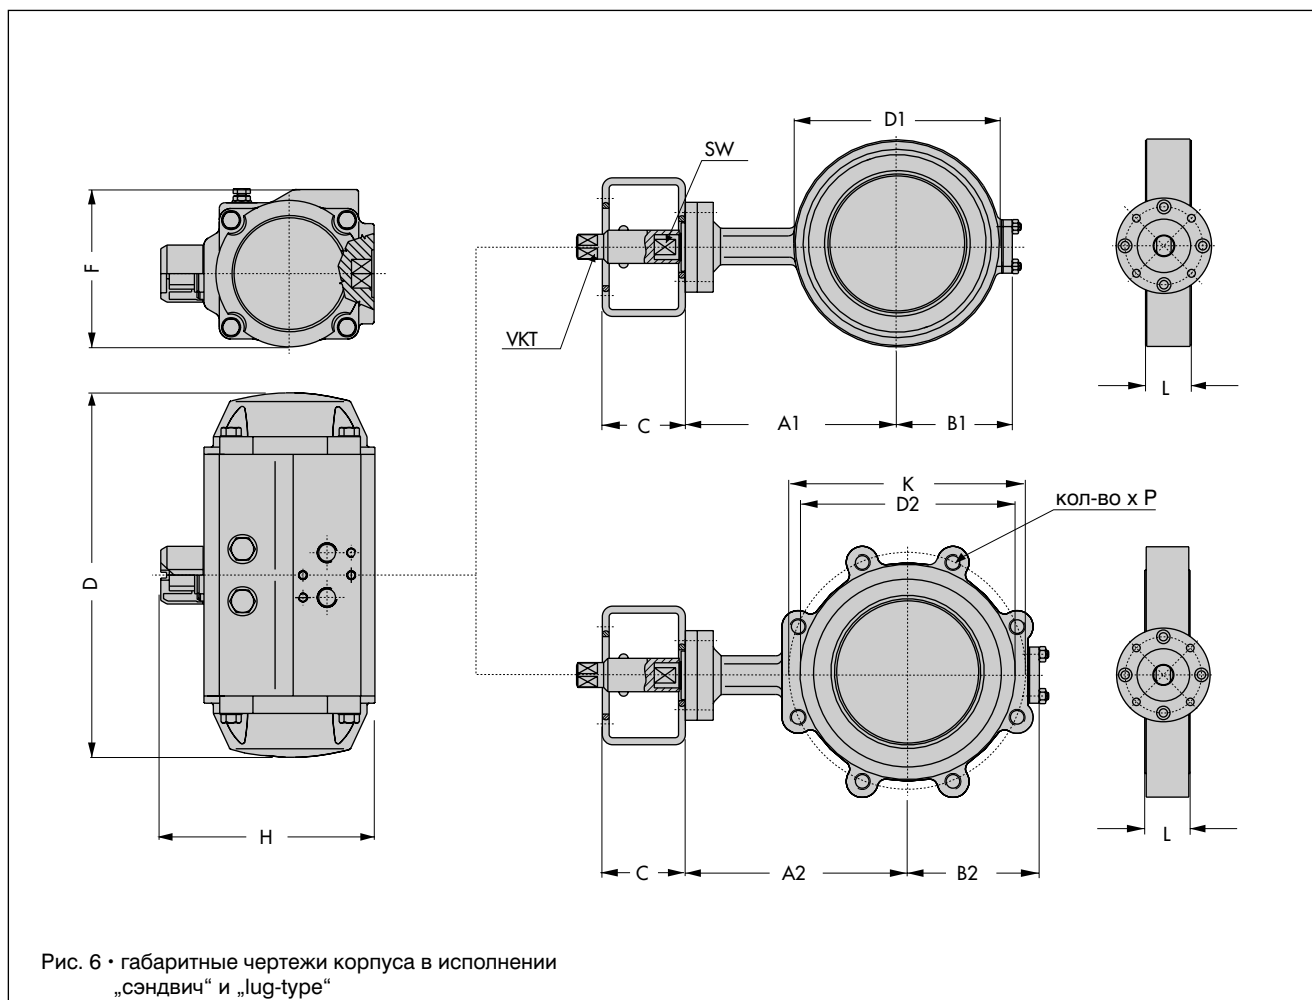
· габаритные чертежи корпуса в исполнении „сэндвич“ и „lug-type“
